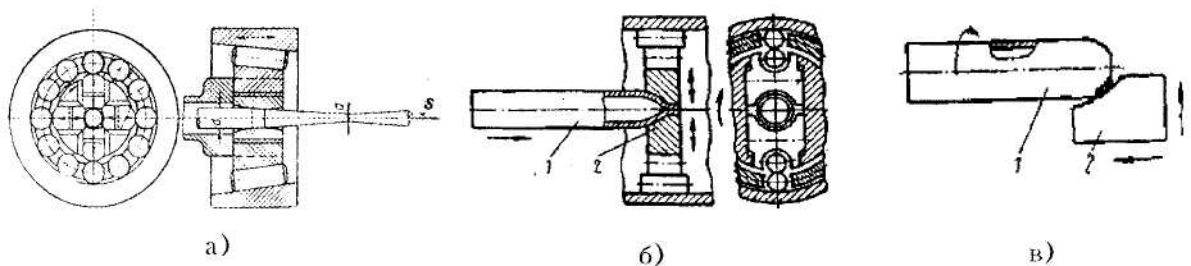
Альтернативні схеми обтиснення: 1 – заготовка; 2 – бойок;
